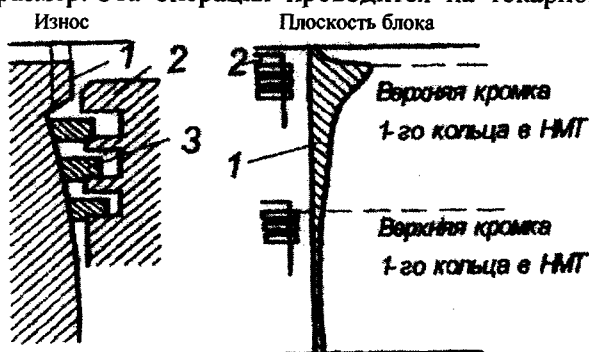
Кривая износа цилиндра компрессора вдоль образующей: ВМТ, НМТ – верхняя и нижняя мертвые точки; 1 – стенка цилиндра; 2 – поршень; 3 – поршневое кольцо
